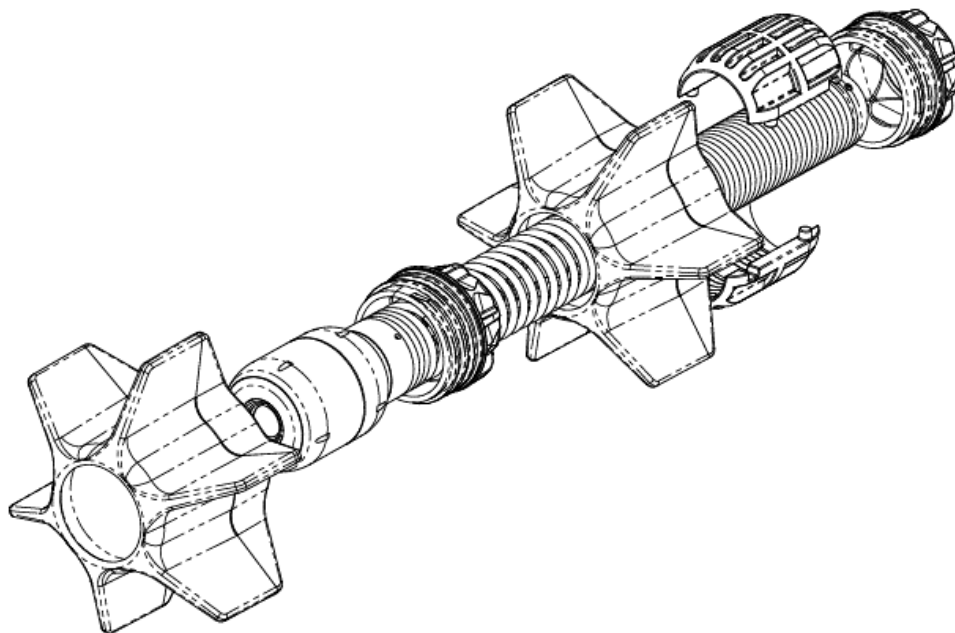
Universeller Kamerakufensatz für 2" (50 mm) Kamera und 1,4" (36 mm) Flexiprobe
